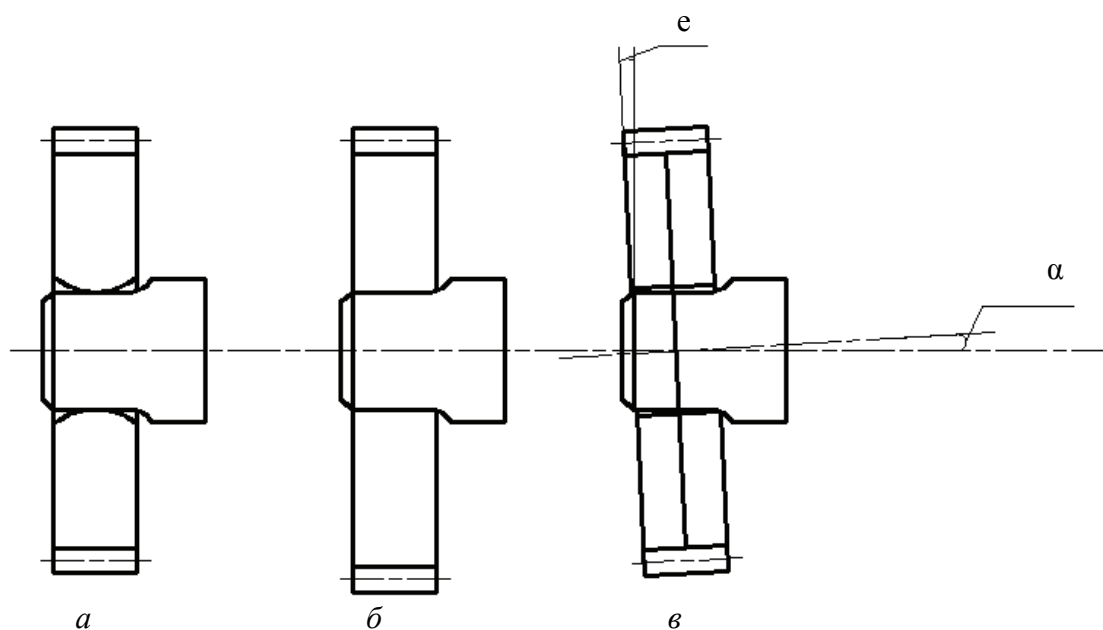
Виды погрешностей при запрессовке зубчатого колеса
